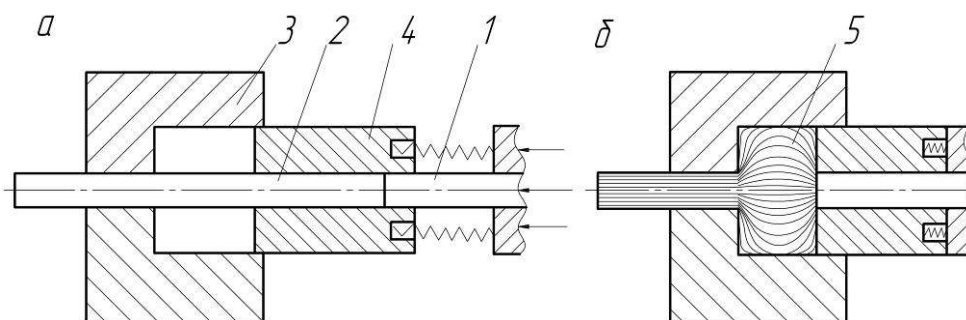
Способ изготовления изделий из длинномерных заготовок
